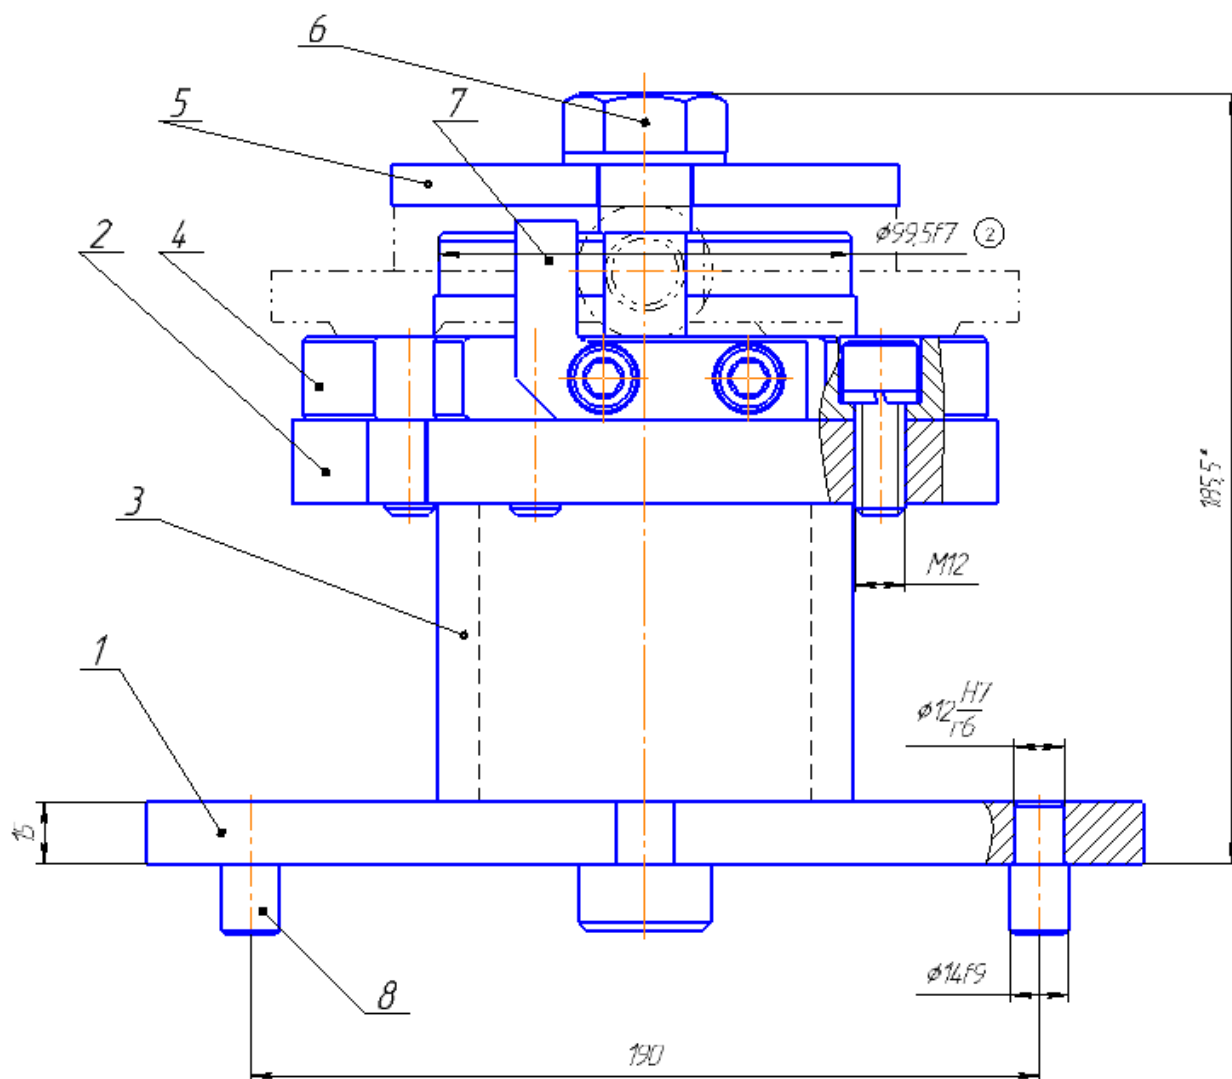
Эскиз приспособления и расположения детали
